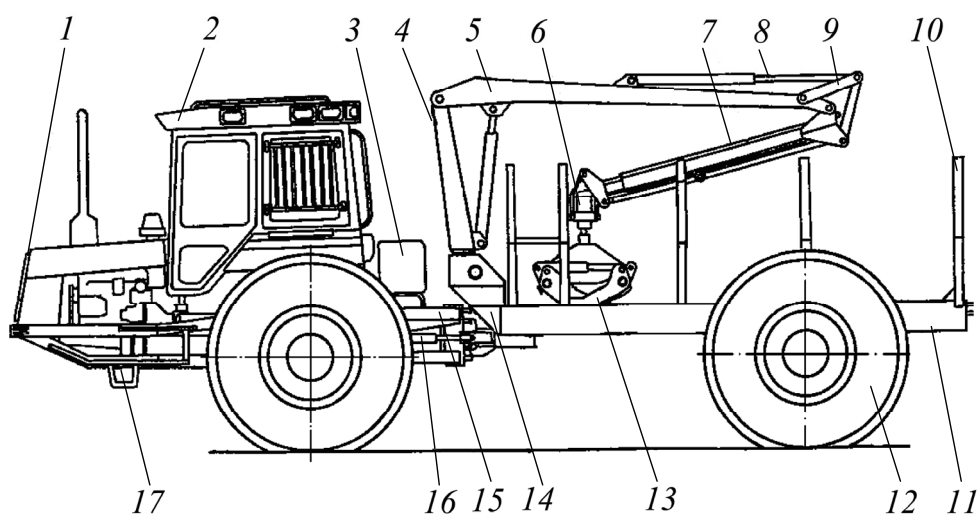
Погрузочно-транспортная машина МЛПТ-354М «Беларус»: 1 – двигатель; 2 – кабина; 3 – бак гидропривода; 4 – колонна; 5 – стрела; 6 – ротатор; 7 – рукоять; 8 – гидроцилиндр управления рукоятью; 9 – четырехзвенник; 10 – стойки; 11 – грузовая платформа; 12 – колесо; 13 – грейфер; 14 – опора вертикально-горизонтального шарнира; 15 – рама; 16 – гидроцилиндр поворота; 17 – подножка
